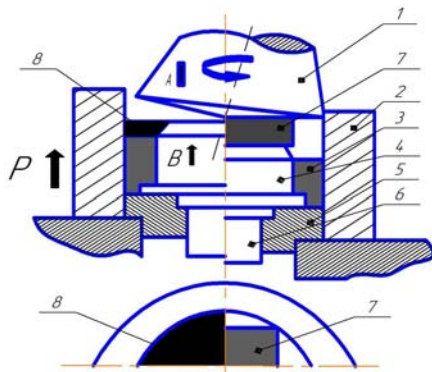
Схема налагоджування для штампування обкочуванням фланцевих деталей та заготовок: 1 - пуансон; 2 - контейнер; 3,4- матриця; 5 - кільце; 6 - виштовхувач; 7 - вихідна заготовка; 8 - готова деталь
